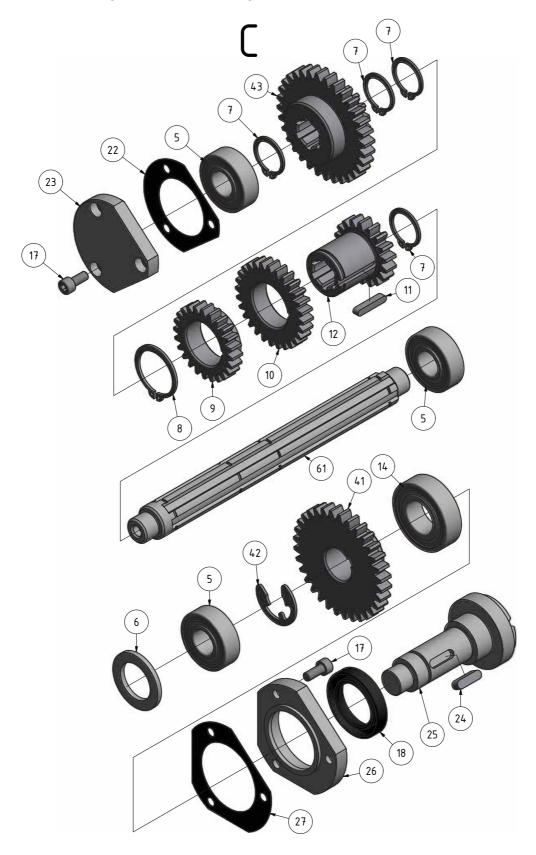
Vorschubgetriebe 5-6 - Feed gear 5-6
